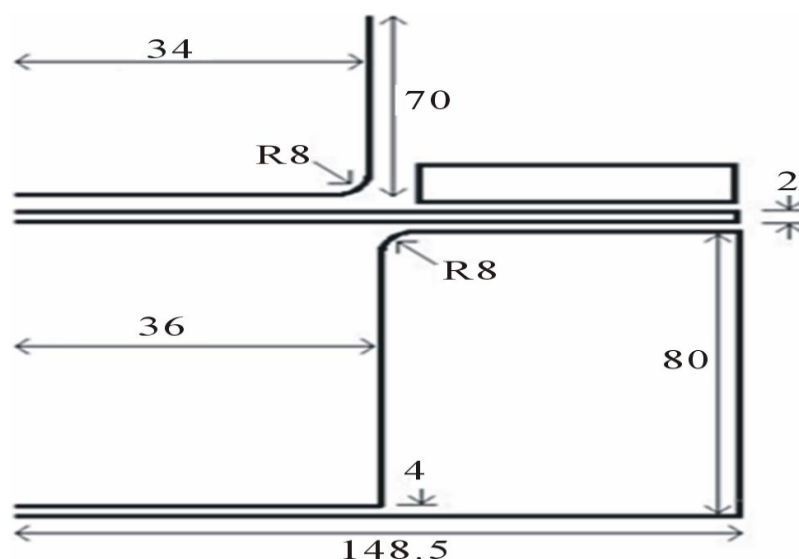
Схема процесса вытяжки цилиндрической чашки
